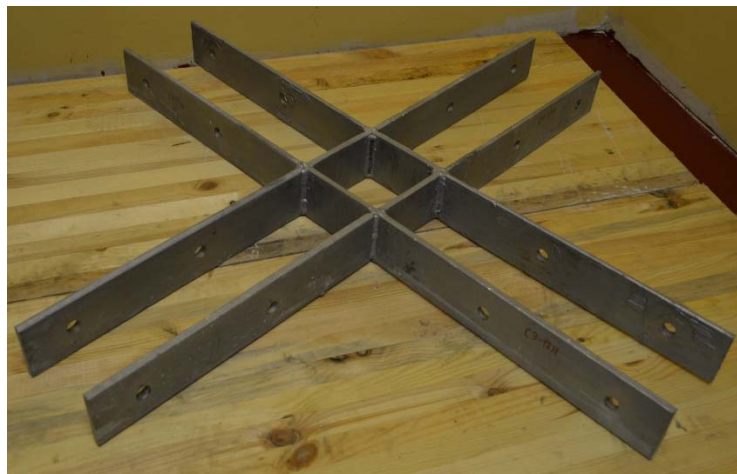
Общий вид соединительного сварного элемента СЭ-1в (СЭ-1н)
